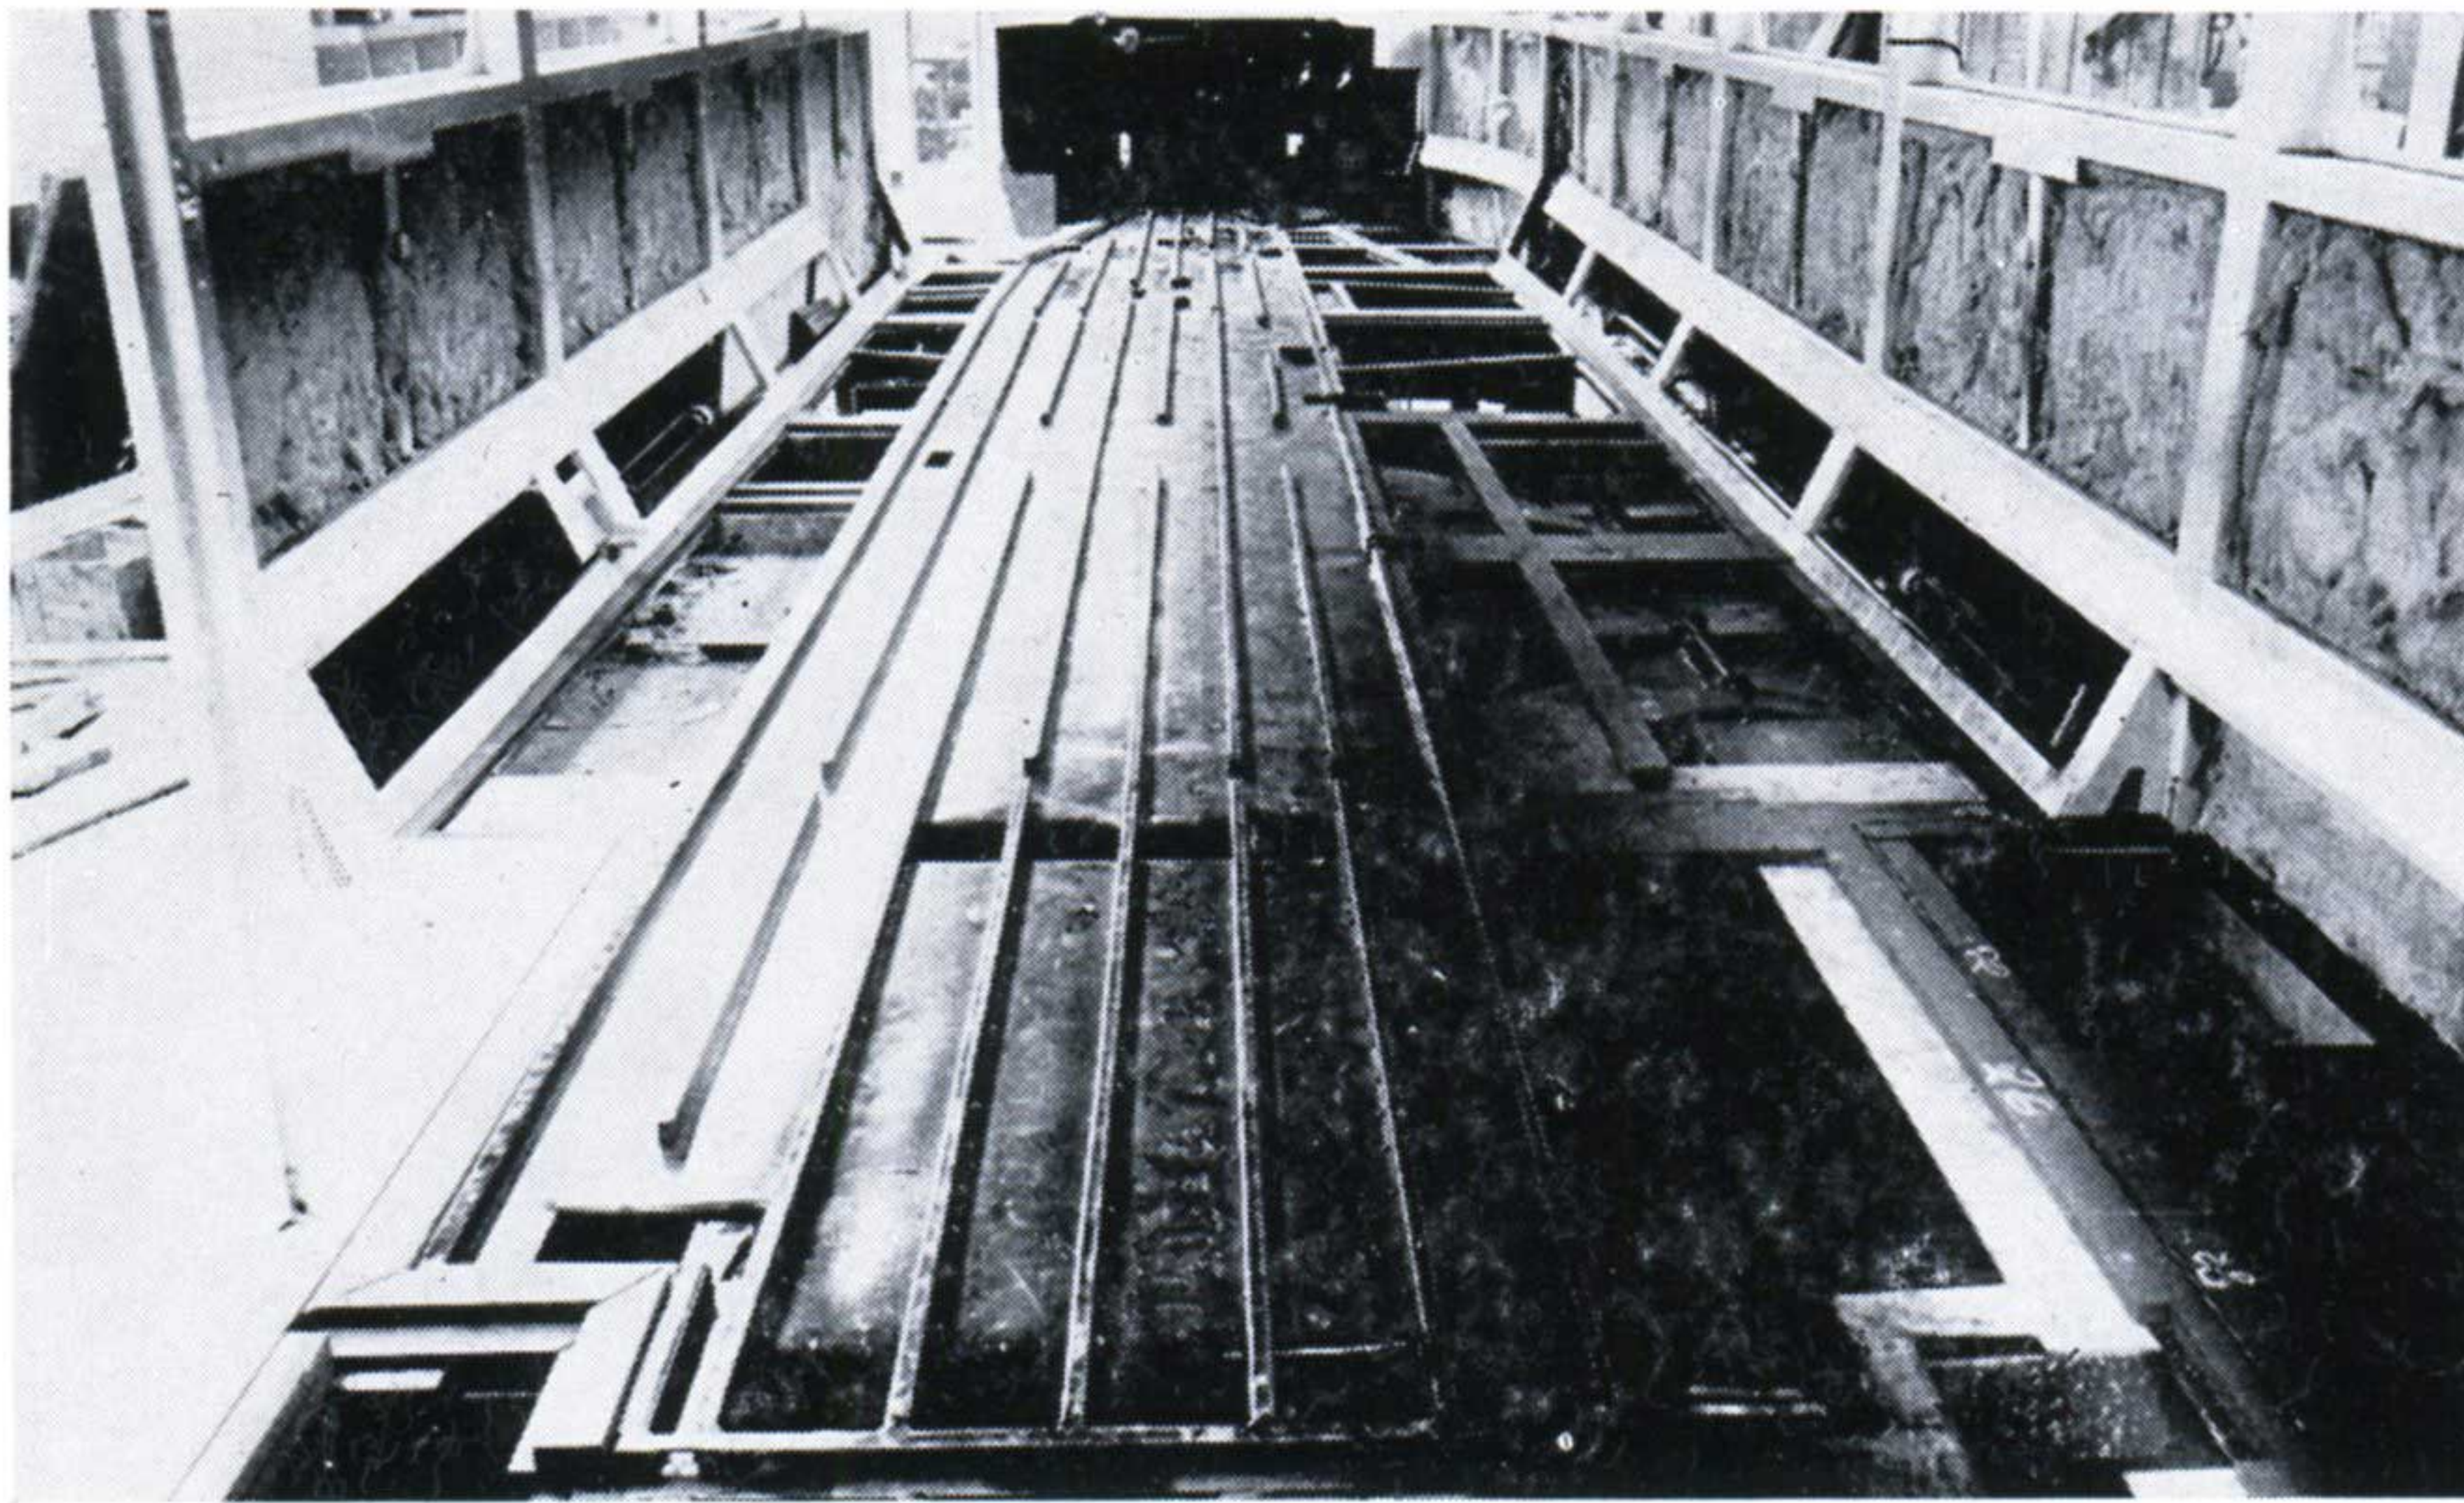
caniveaux à câbles dans le plancher de la voiture
